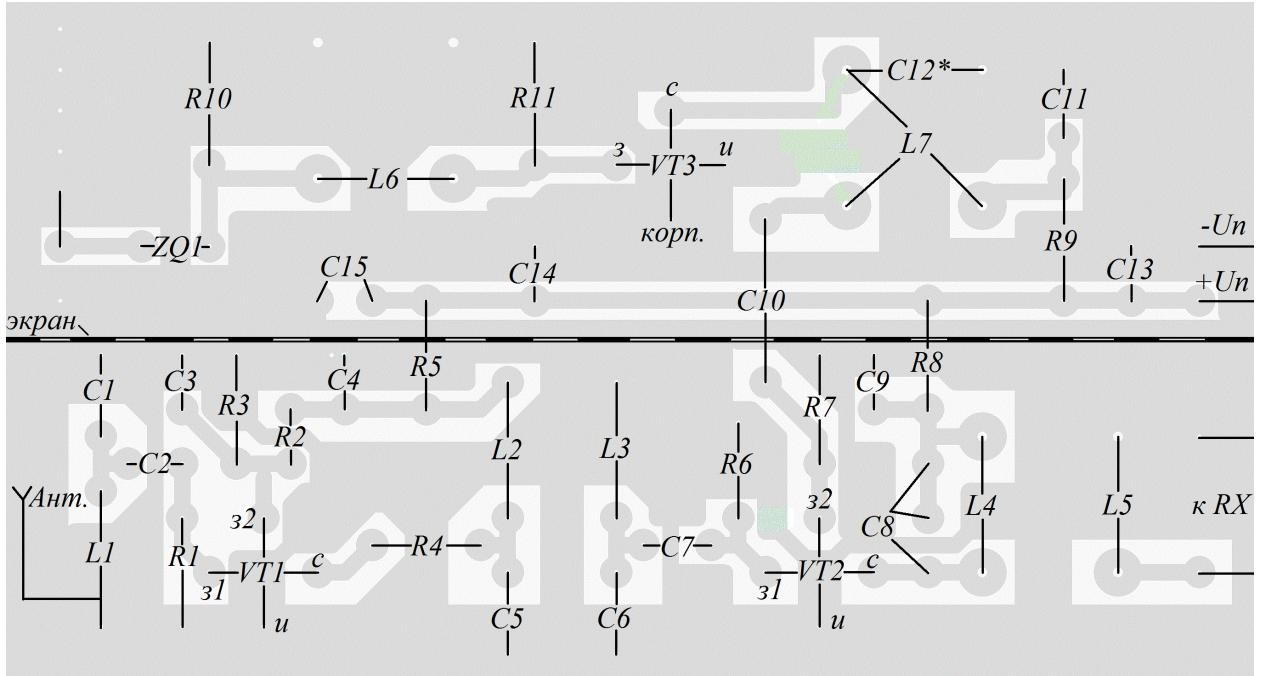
Эскиз монтажной платы конвертера. Вид со стороны установки деталей
